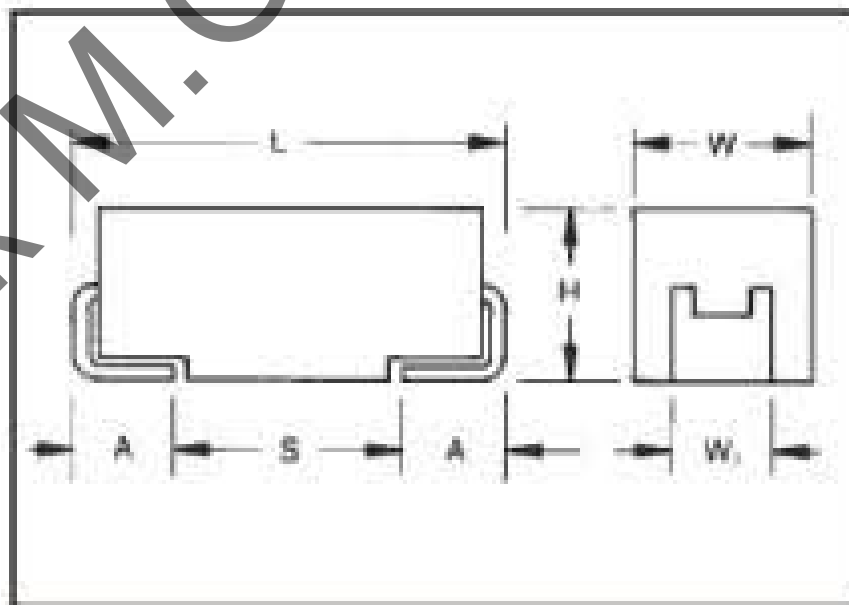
Розміри конденсатора стандартної серії ТАJ у корпусі 6032
